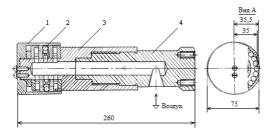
Схема инструмента для поверхностной пневмовибродинамической обработки наружных рабочих поверхностей нежестких деталей типа тел вращения: I-стакан; 2-деформирующие шары; 3-инструмент для ПВДО; 4-оправка для закрепления инструмента для ПВДО
